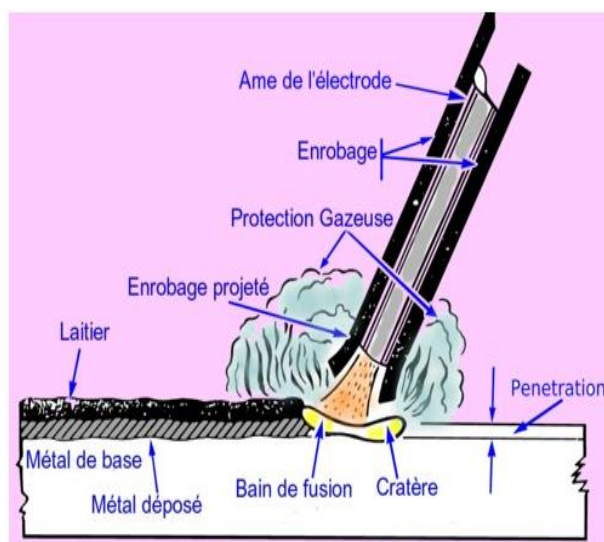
Schéma d'assemblage par soudage .
